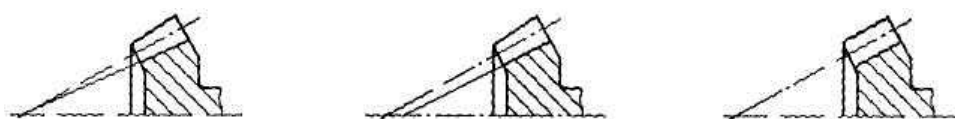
Осевая форма зуба конического зубчатого колеса
